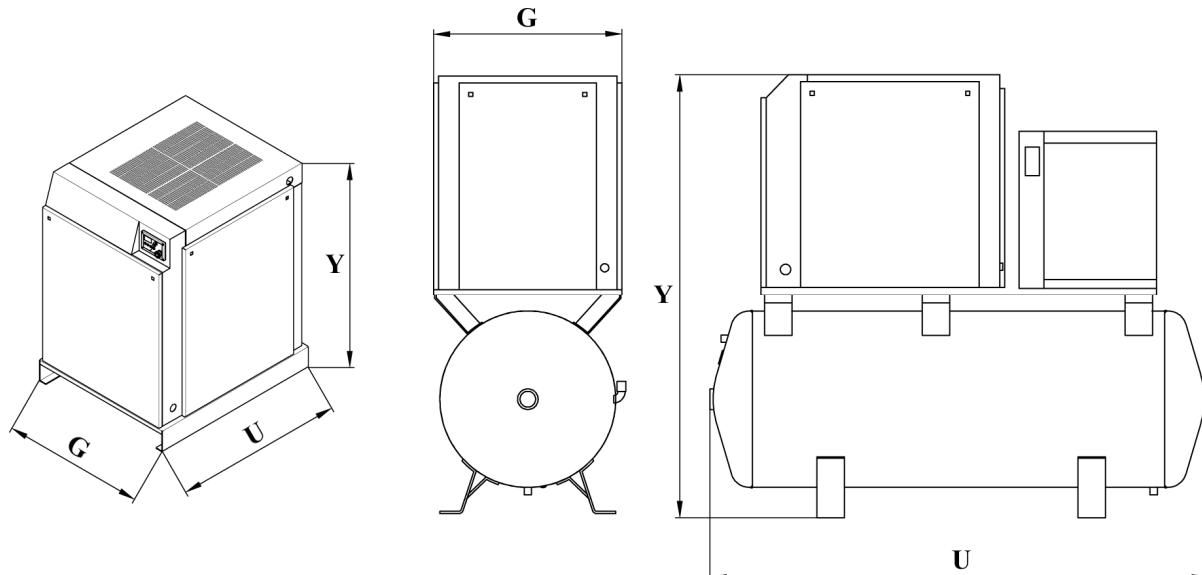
DMD SINGLE (C) & DMD НА БАКЕ (CR & CRD), РАЗМЕРЫ КОМПРЕССОРА
